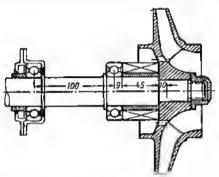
Disposición de los spoyos del árbol del rotor de álabes
